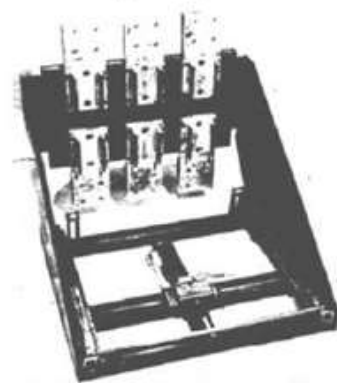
Внешний вид автомата AR с установочным устройством.
